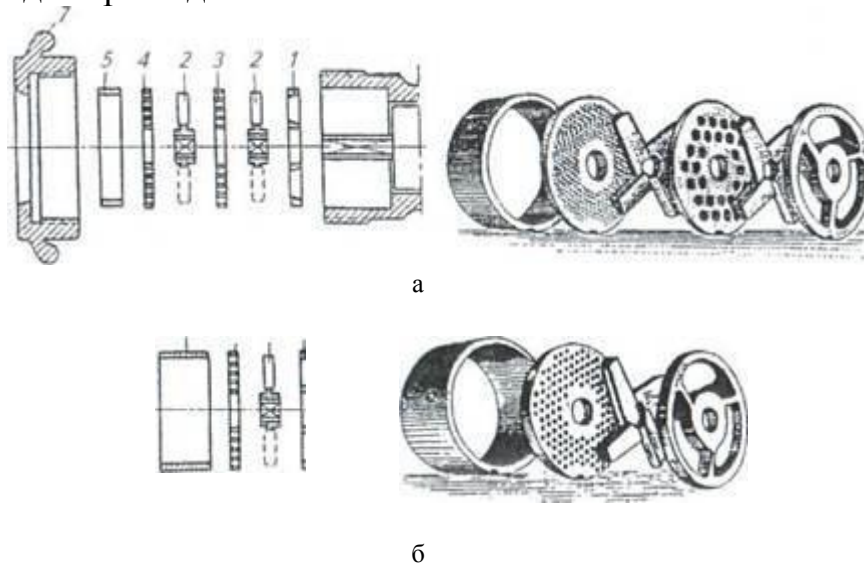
Схемы сборки режущего механизма волчка:
